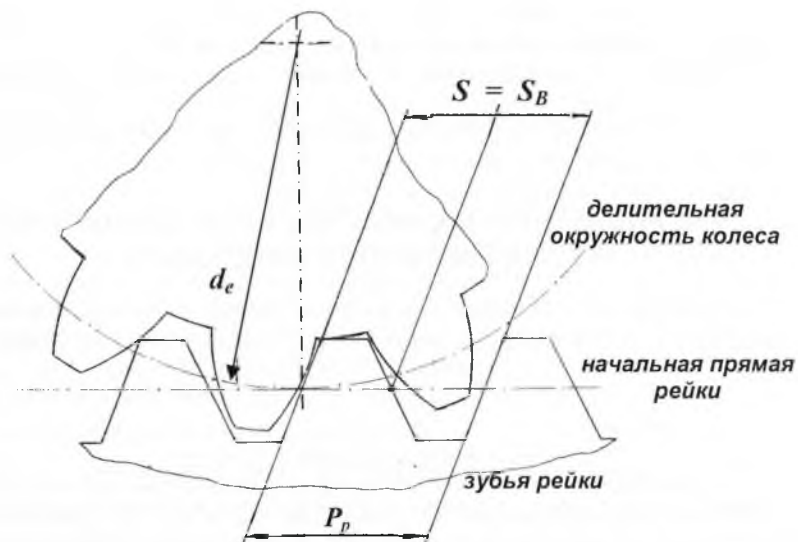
Схема реечного зацепления: P_p – шаг зубьев рейки; S – толщина зуба рейки; S_B – ширина впадины между зубьями рейки; d_e – делительный диаметр зубчатого колеса.
